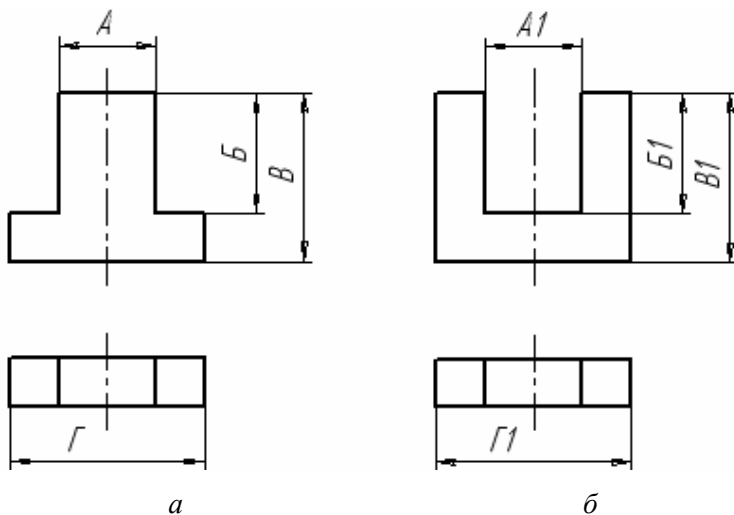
Кресленик деталей з однаковими виглядами зверху
